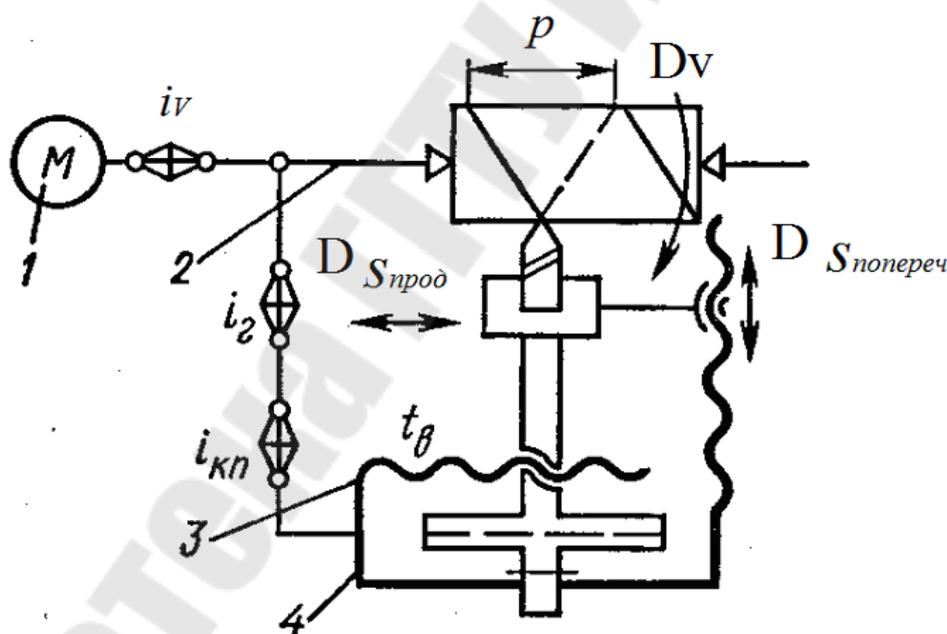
Структурная схема токарно-винторезного станка
